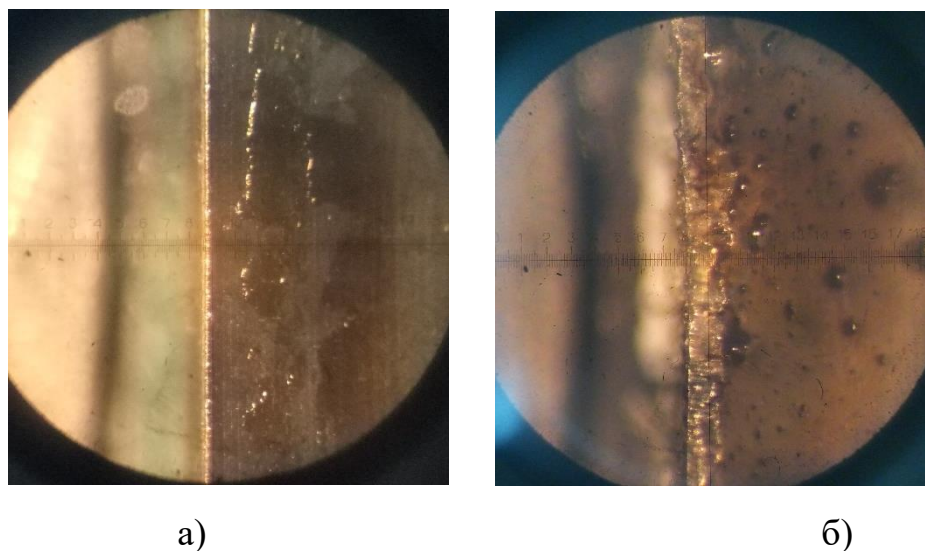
Износ режущих кромок периферийной пластины:
